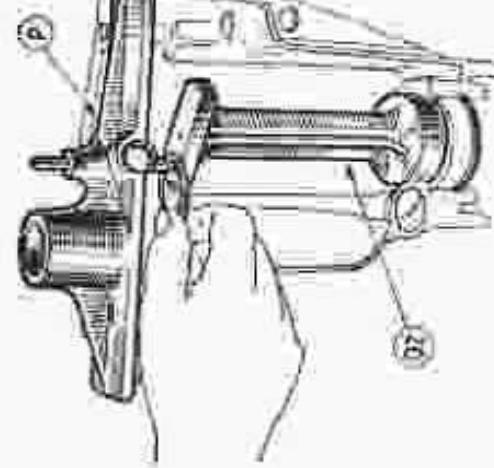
Montage de l'arbre de la bague à l'aide d'un calibre P.
